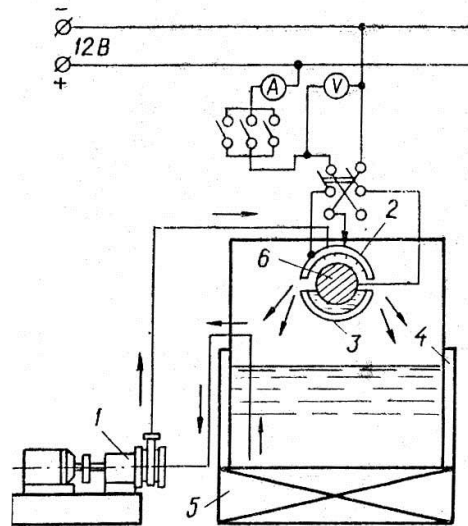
Схема установки для електролітичного покриття шийок вала:
